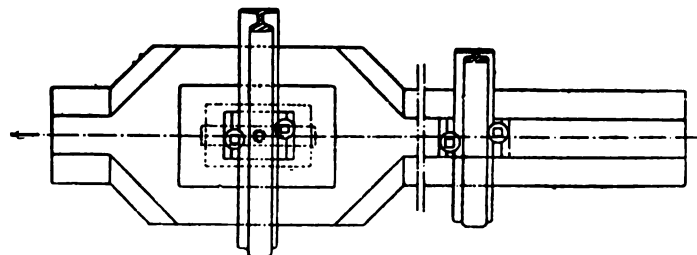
Traverse Thiollier-Bigazzi. - Pianta.
